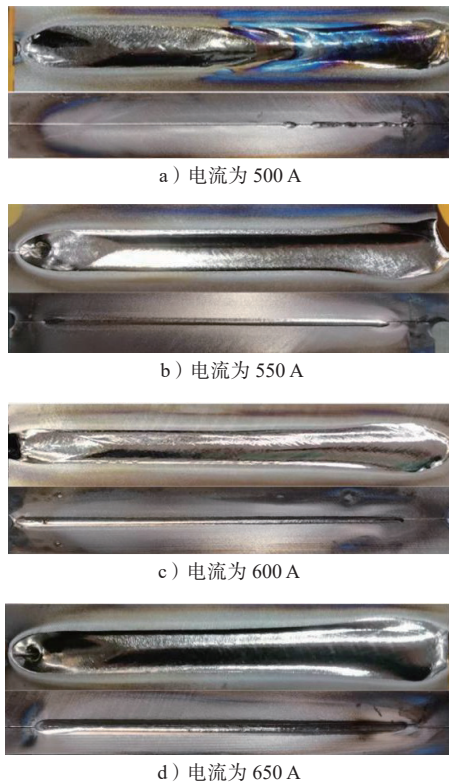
不同焊接电流条件下的焊缝表面形貌
